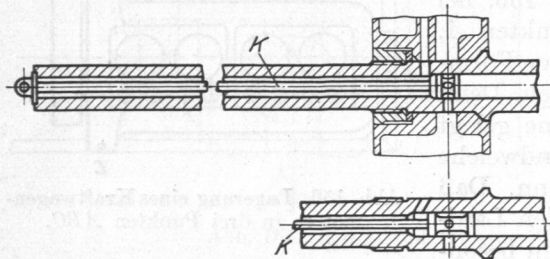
und 159. Gekühlte Kolbenstange einer Großgasmaschine.
